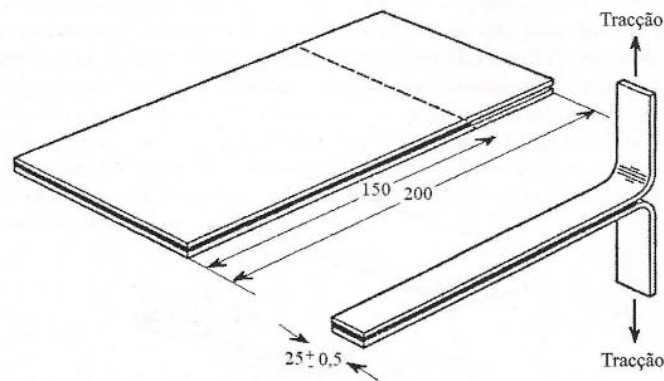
Provete para ensaio de arrancamento em junta T (dimensões em mm).
